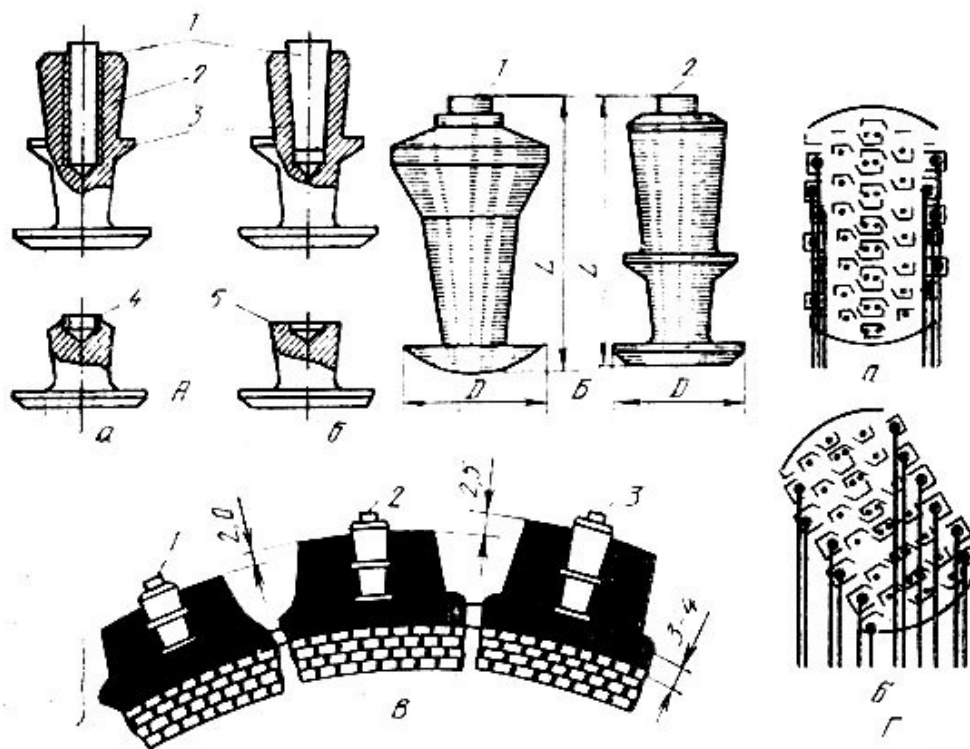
Шипы: А — шипы с впаянным (а) и запрессованным (б) стержнями: 1 — стержень, 2 — припой, 3 — корпус, 4 — остаток припаянного стержня при изношенном корпусе, 5 — выпавший из гнезда запрессованный стержень заставил корпус изнашиваться вместе с протектором; Б — однофланцевый 1 и двухфланцевый 2 шипы: L — длина шипа, D — диаметр фланца; В — для протекторов разной высоты можно подобрать шипы разной длины; 1 — шип P8—2—110, 2 — шип P8—2—130, 3 — шип P8—2—155; Г — при торможении (а) шипы оставляют на льду меньше борозд, чем при заносе (б).
